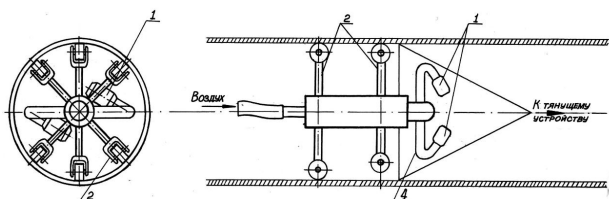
Схема установки для удаления пыли с поверхности трубы после очистки
